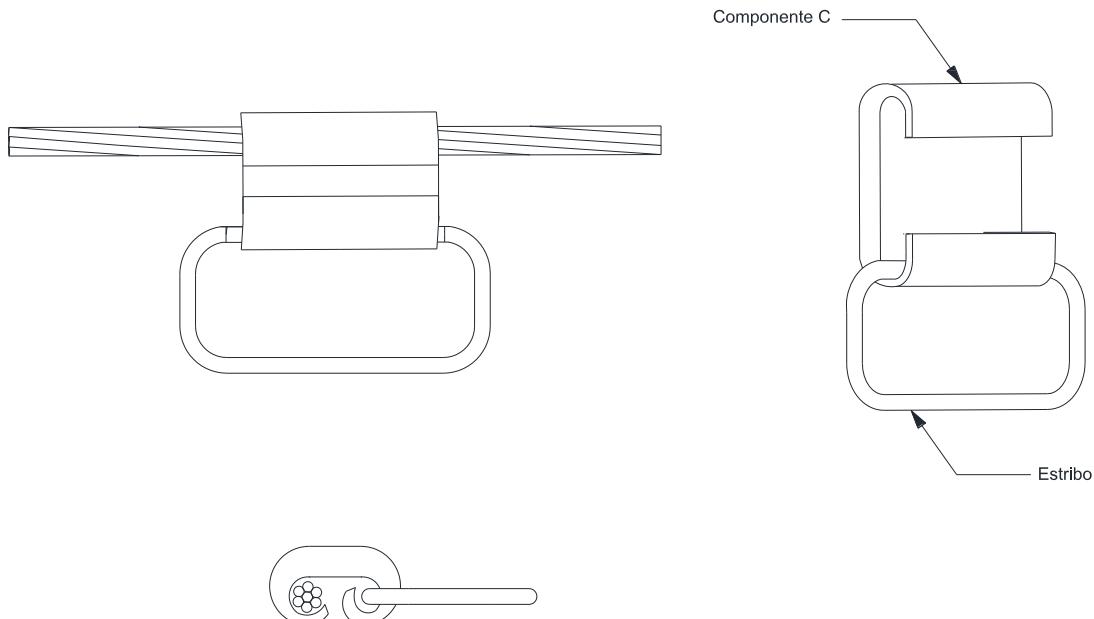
Conexões e emendas – Conector de compressão tipo “C” com estribo
